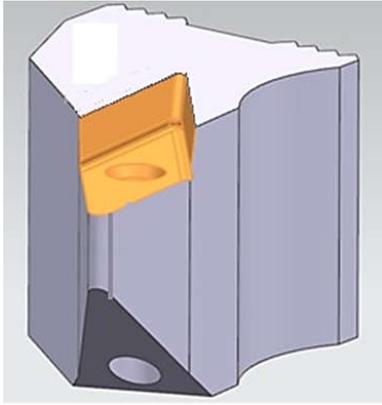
Рабочие поверхности корпусов режущего инструмента - поверхности гнезда под СТП
